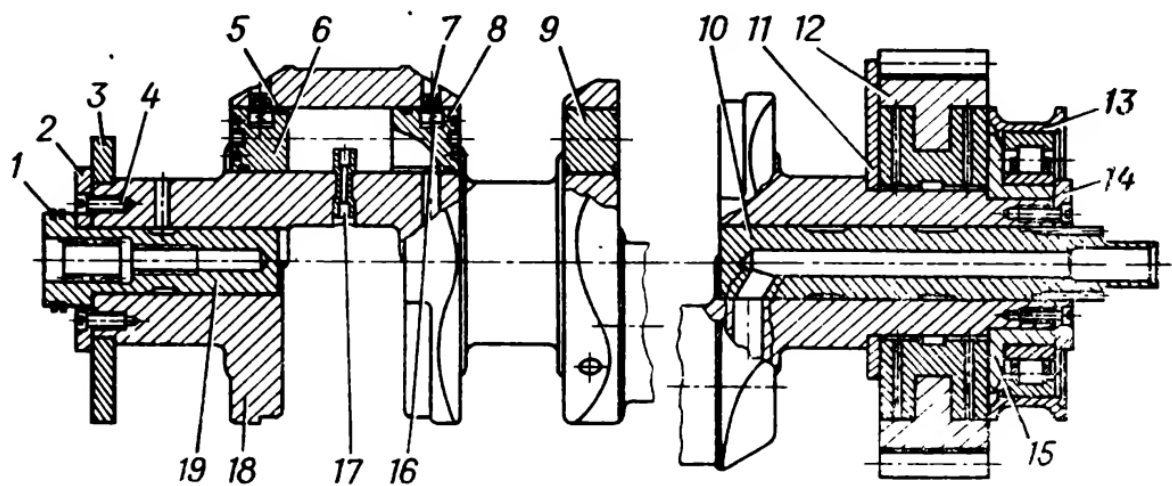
Впускний колінчастий вал: 1 – кільце; 2 – скоба; 3, 11 – знімний противагу; 4 – гвинт; 5 – кільце ущільнювача; 6 – заглушка; 7 – фіксатор; 8 – заглушка; 9 – проставка; 10, 19 – хвостовики; 12 – пружна муфта; 13 – стакан підшипника; 14 – скоба; 15 – проставка; 16 – пружина; 17 – жиклер; 18 – впускний колінчастий вал
